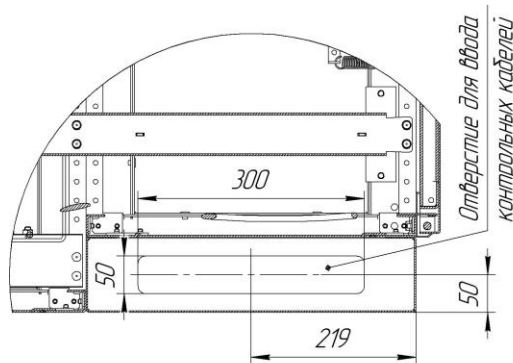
Установка СЭЩ-70-35 на фундамент с кабельным каналом
